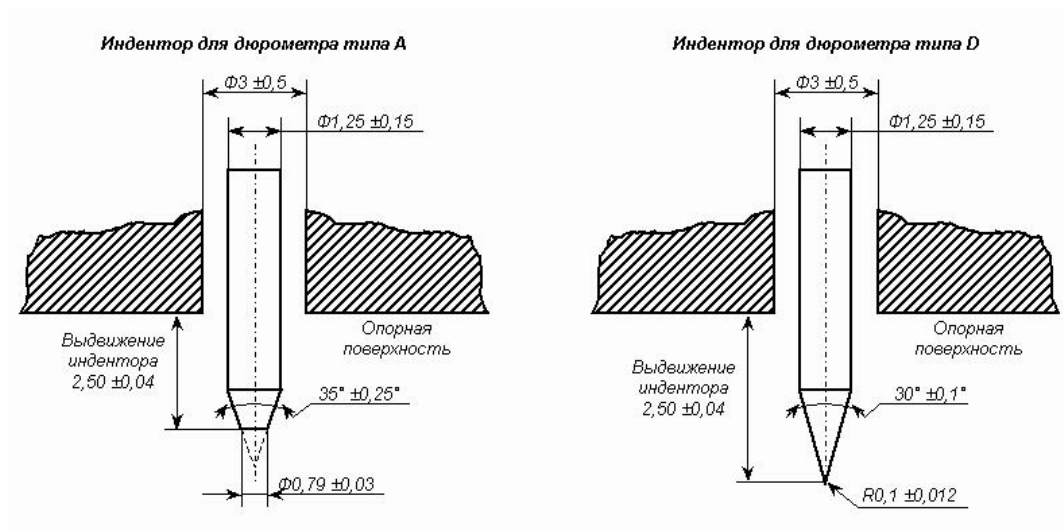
Чертёж инденторов для дюрометров типов А и D
